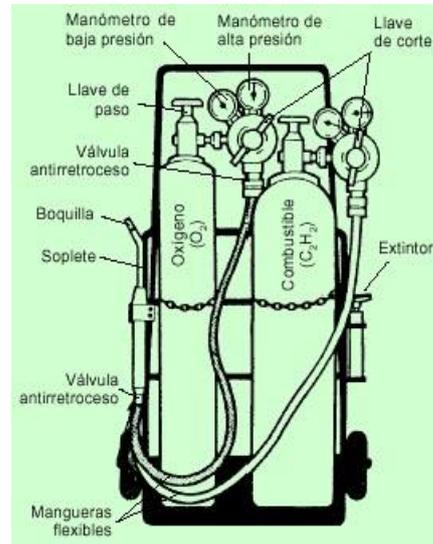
Elementos principales de una instalación móvil de soldadura por gas
